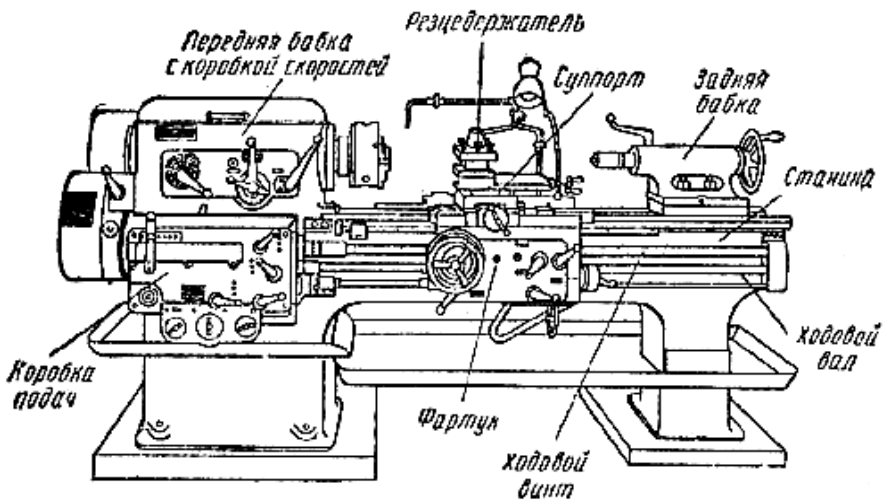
Токарно-винторезный станок с коробкой скоростей.
